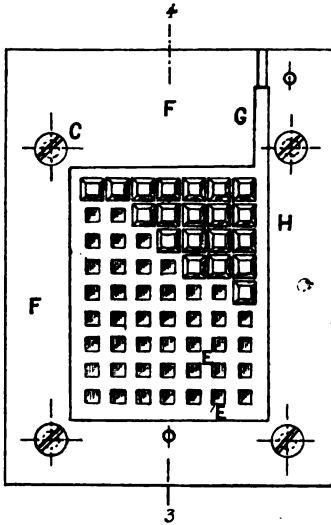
Moule L. Champagne. FIG. 178. — Coupe du moule L. Champagne.
